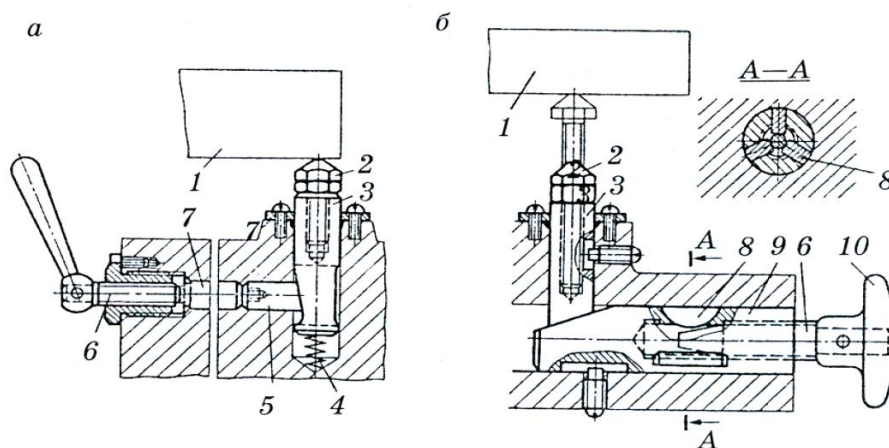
Вспомогательные опоры: а – самоустанавливающаяся опора; б – клиновая опора; 1 – заготовка; 2 – опора; 3 – плунжер; 4 – пружина; 5 – промежуточный сухарь; 6 – винт; 7 – стержень; 8 – шпонка; 9 – горизонтальный клин; 10 – рукоятка
